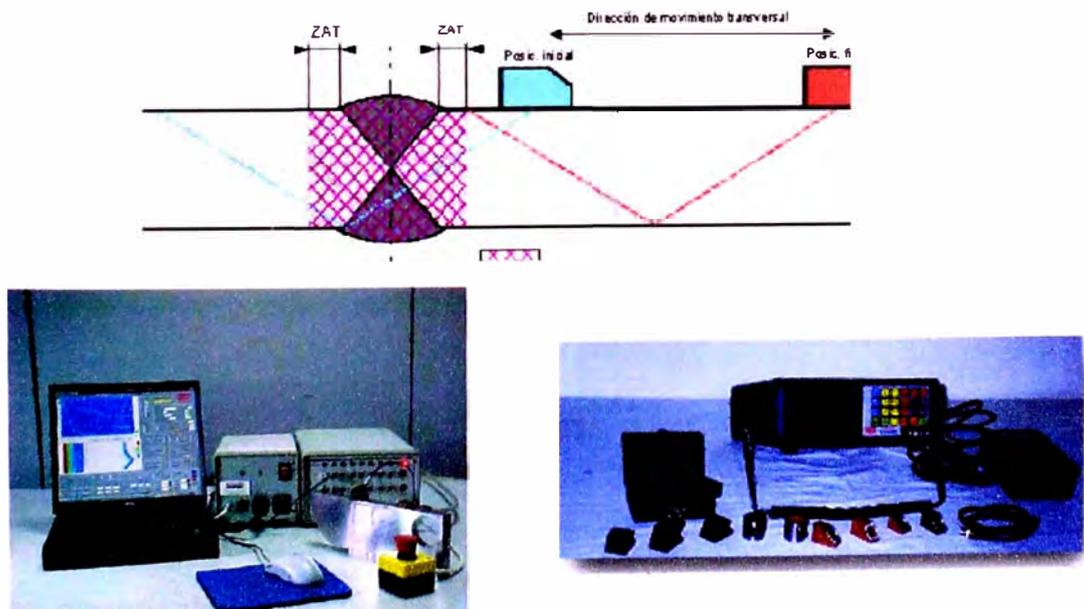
Inspección ultrasónica de soldaduras
